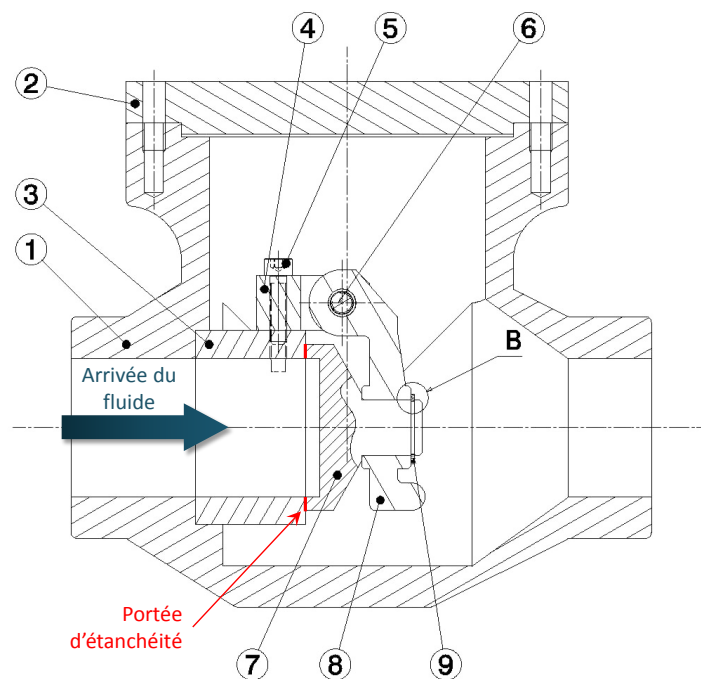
Plan d'un clapet anti-retour [VALLET, 08]
